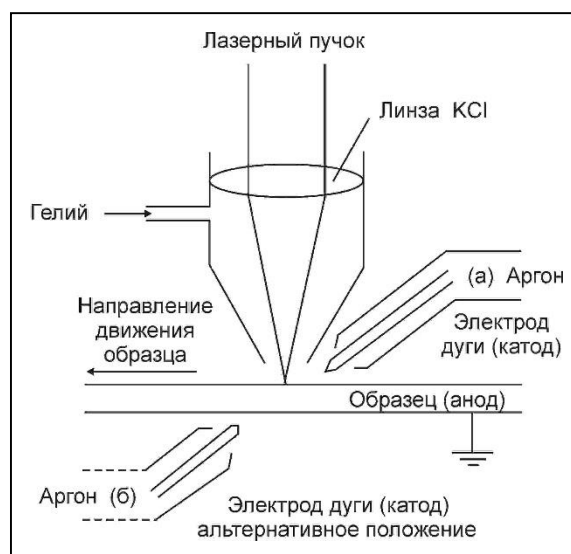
Схемы реализации лазерно-дуговых процессов сварки и резки с расположением лазерного пучка и дуги с неплавящимся электродом с одной стороны изделия (а) и с разных сторон (б) [5].
